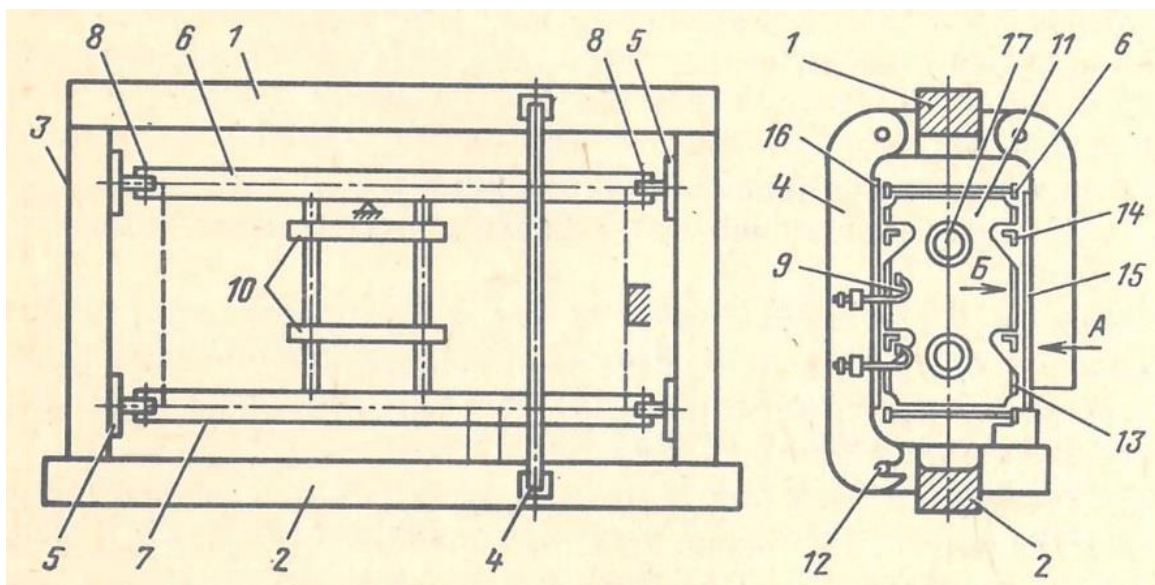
Сборочное приспособление (СП) для кессона с базированием по поверхности каркаса: 1, 2 – балки; 3 – стойка; 4 – рубильник; 5 – фиксатор; 6, 7 – лонжероны; 8 – штифт; 9 – прижим; 10 – опора; 11 – нервюра; 12 – зажим; 13 – отверстие; 14 – стрингер; 15, 16 – обшивки; 17 – отверстие облегчения.
